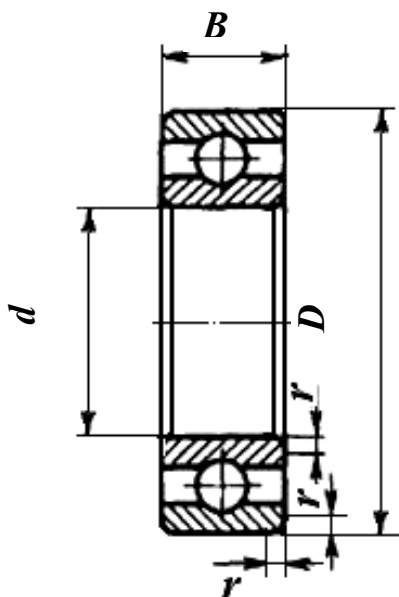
Основные размеры подшипника шарикового радиального однорядного
